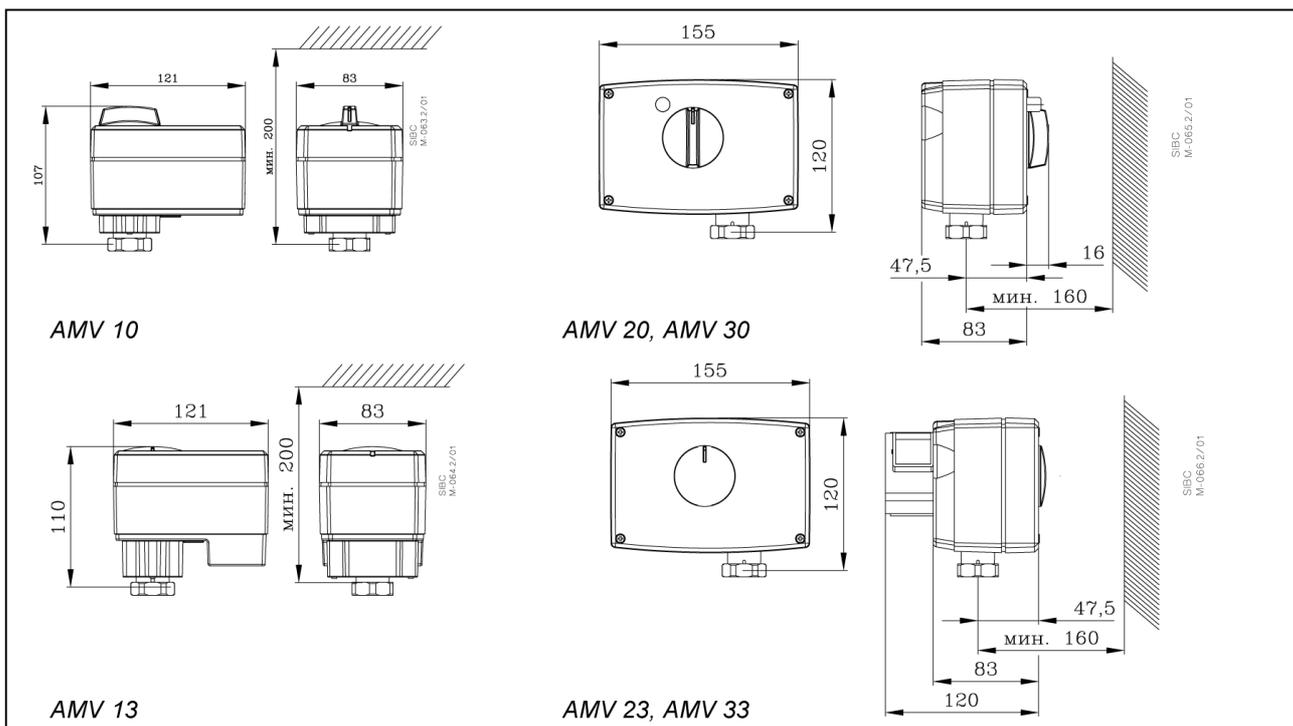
Габаритные и присоединительные размеры AMV 10, 20, 30, 13, 23, 33.
